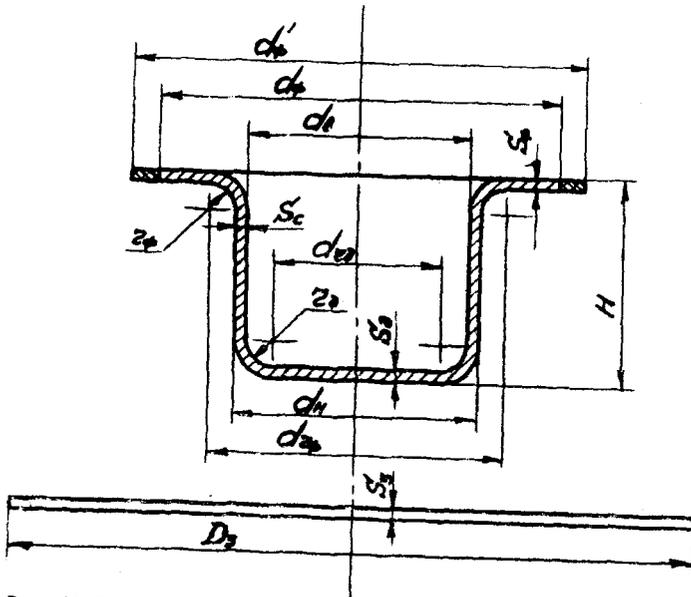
Цилиндрическая деталь с фланцем, полученная вытяжкой (к расчету диаметра заготовки)
